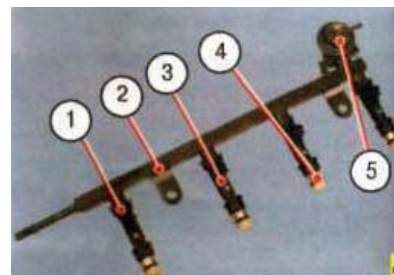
Топливная рампа: 1 - фиксатор форсунки; 2 - рампа; 3 - форсунка; 4 - уплотнительное кольцо форсунки; 5 - регулятор давления топлива
